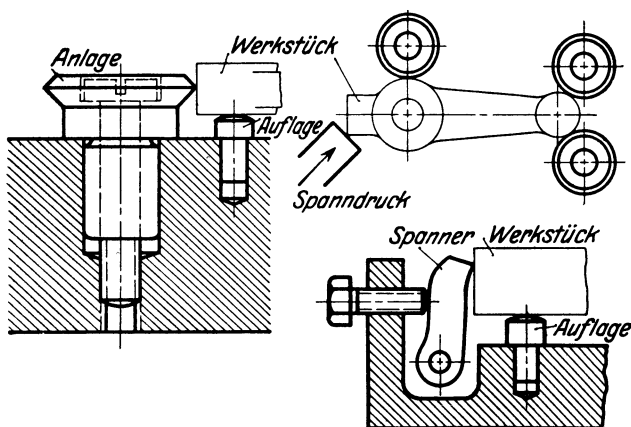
Beispiele der Normung. Von obiger Abbildung sind genormt: Anlage, Auflage, Spanner, sämtl. Schrauben und Gelenkbolzen. Der Körper ist aus genormten Gußeisenstücken gearbeitet.
